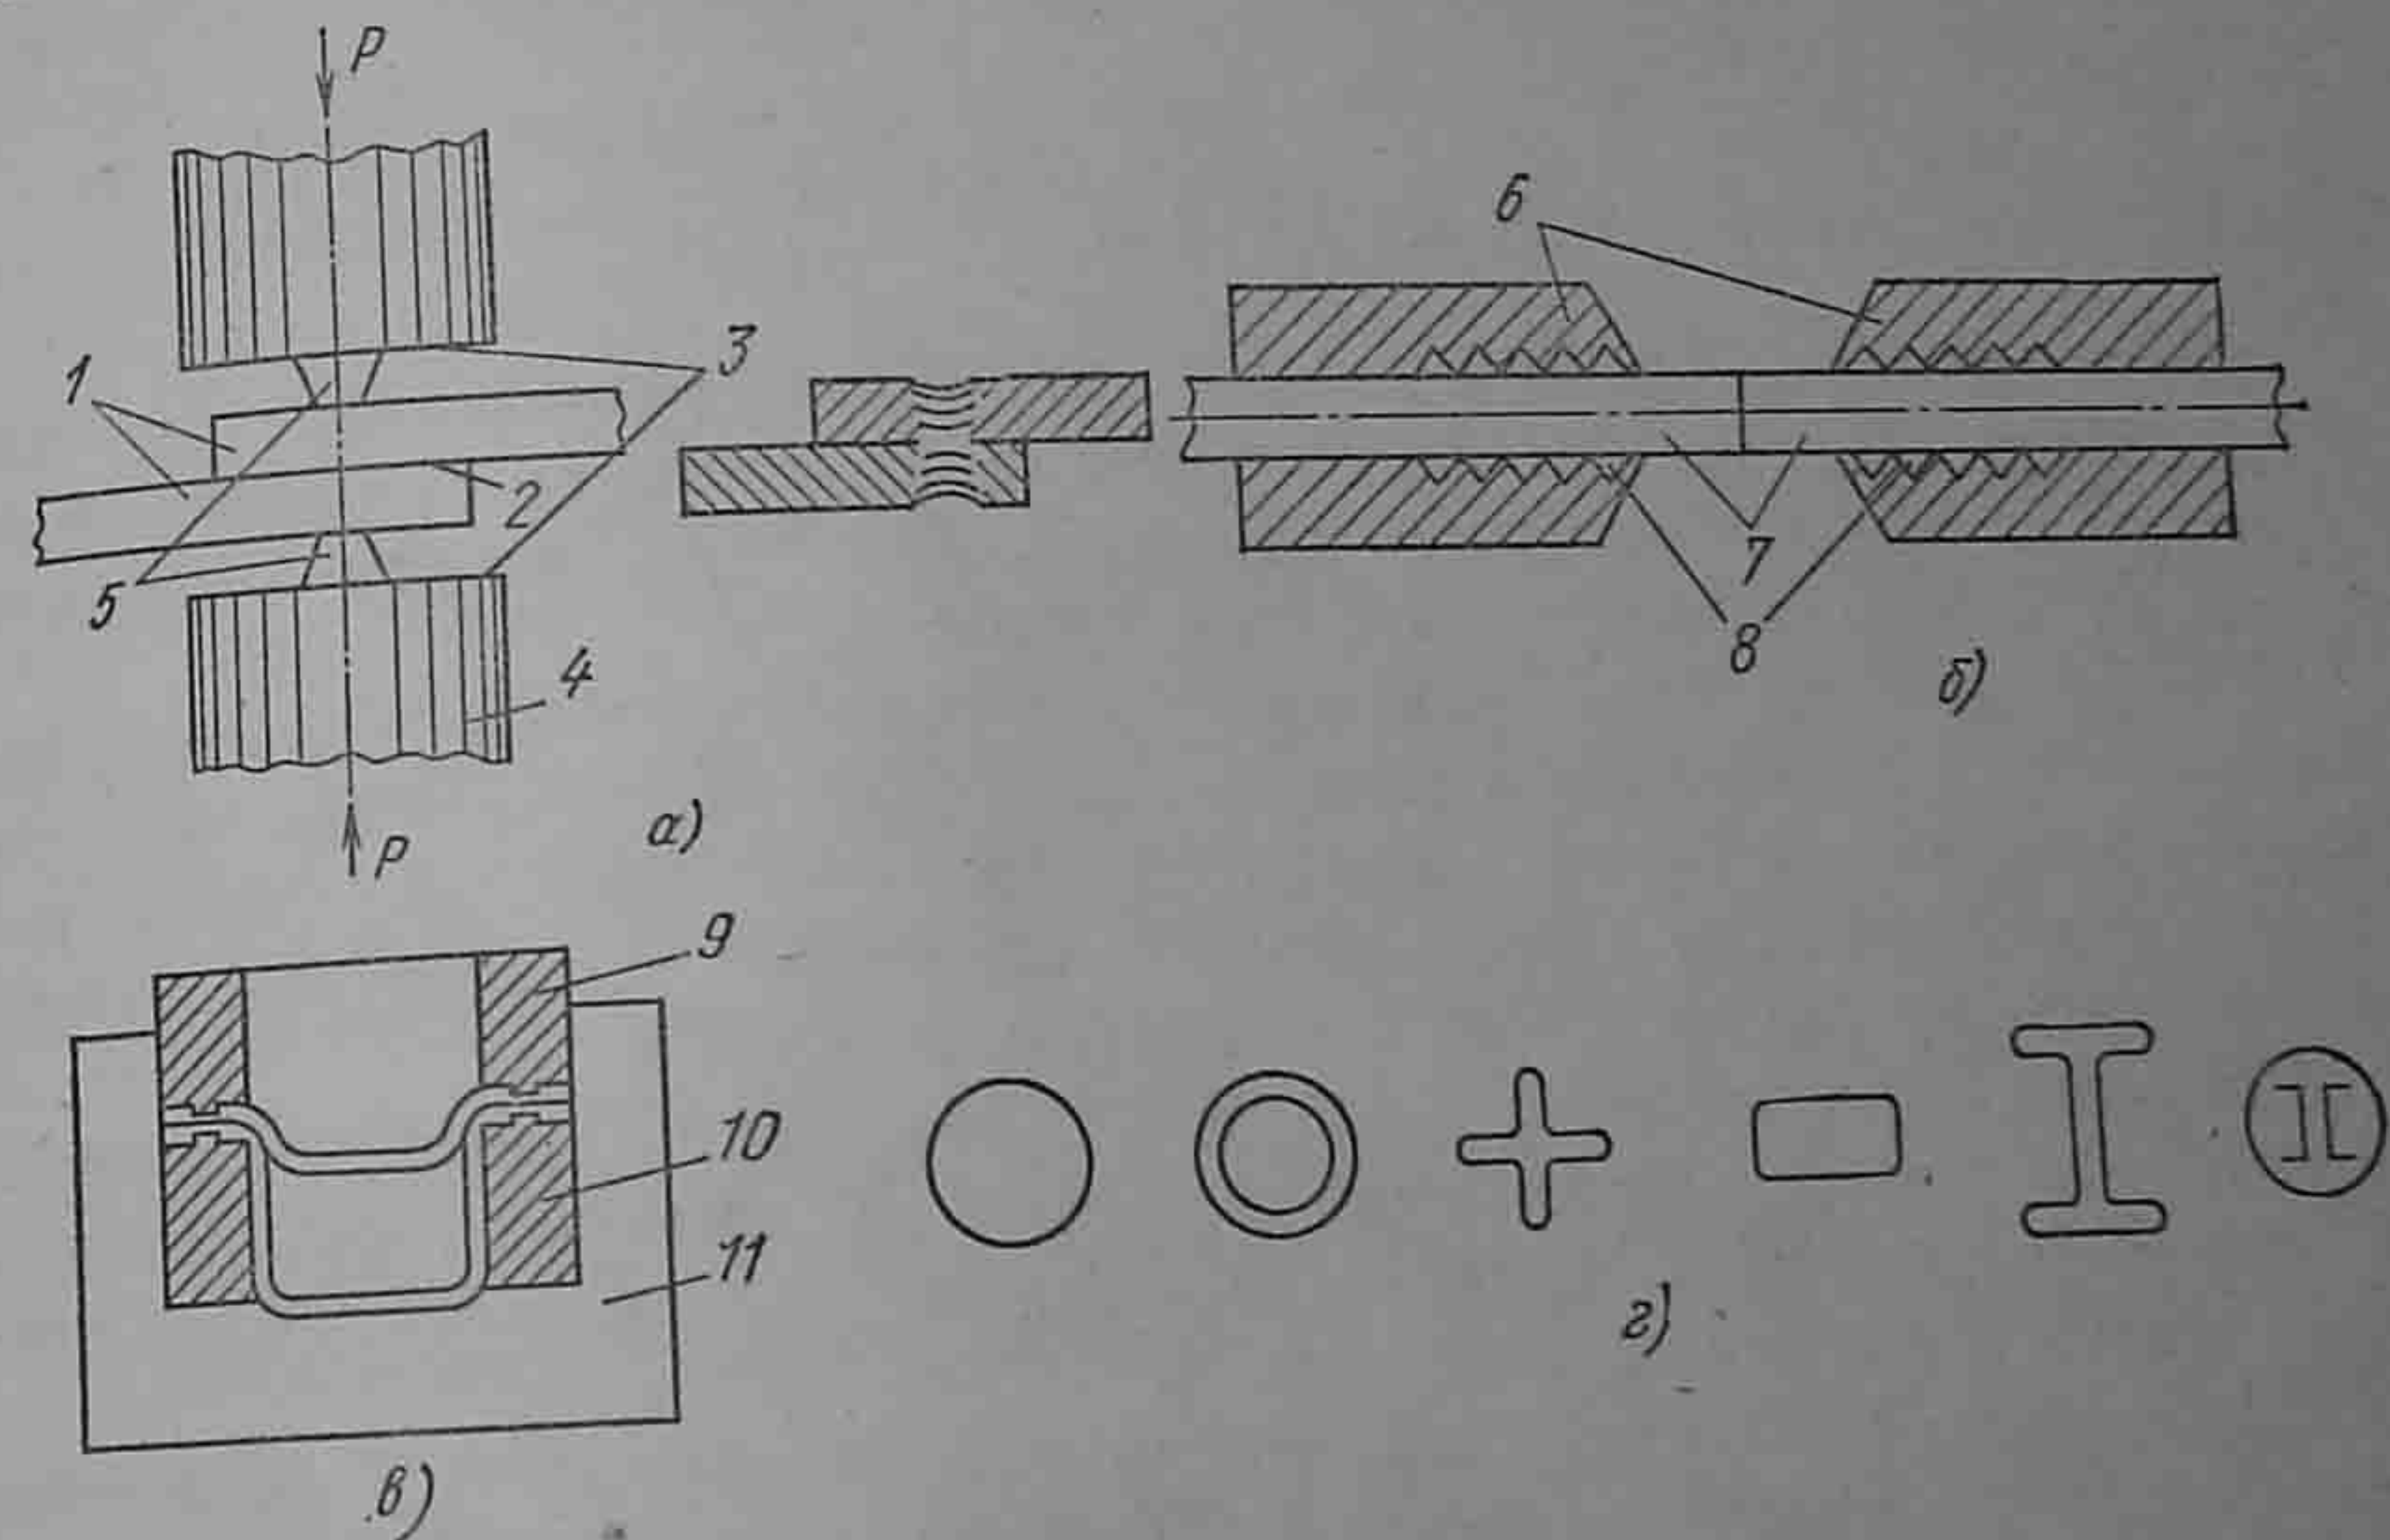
Принципиальная схема холодной сварки: а — точечная; б — стыковая; в — по контуру; г — форма сварной точки
